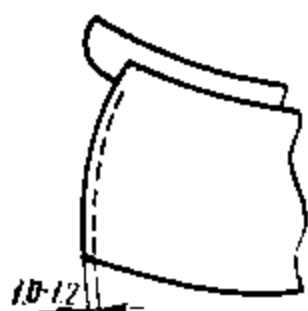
Сборка пяточной части полуботинка тачным швом
